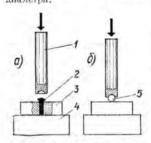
Приспособление для изготовления закленов (п) и способ формовки углубления в обжимке (б): 1 обжимка: 2— заготовка закленки; 3— пластина: 4 стальная плита; 5— стальной шарик.
